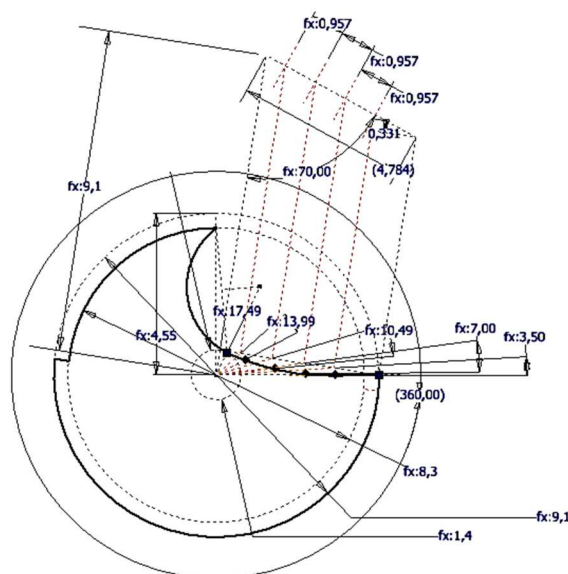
Торцевий переріз стружкової канавки свердла (вихідний)
